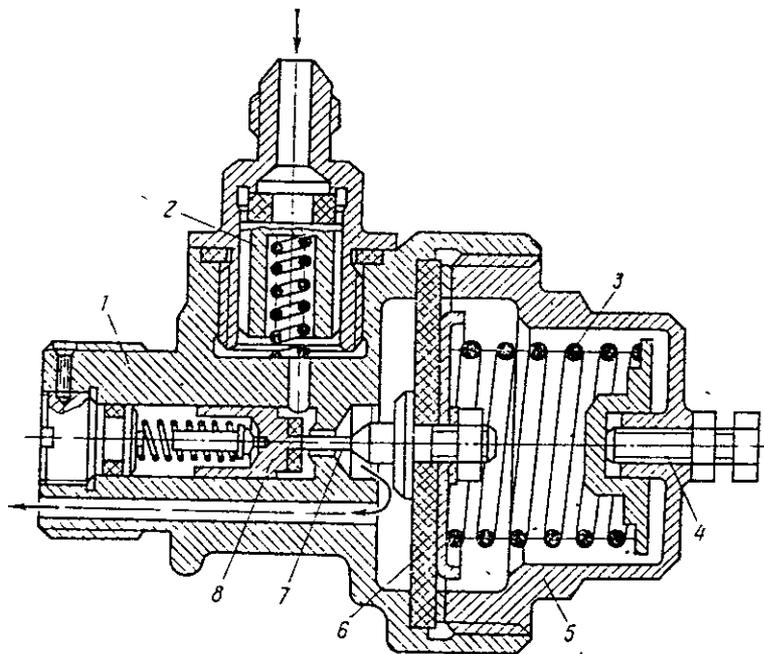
Редуктор Н5810-700М системы наддува гидробака: 1 — корпус; 2 — выпускной клапан; 3 — пружина; 4 — регулировочный винт; 5 — крышка; 6 — мембрана; 7 — шток; 8 — клапан
